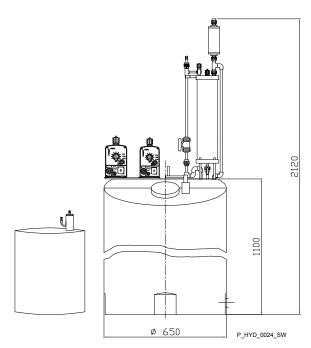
Hoja de dimensiones de Hidracina 250 l (dimensiones en mm)
